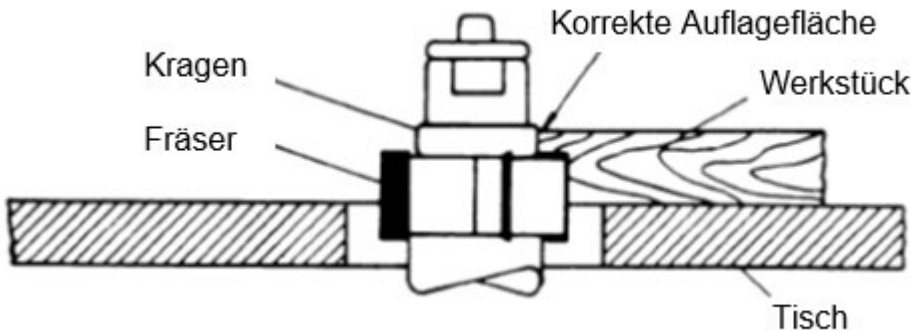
Korrekte Auflagefläche beim Formfräsen mit Kragen
